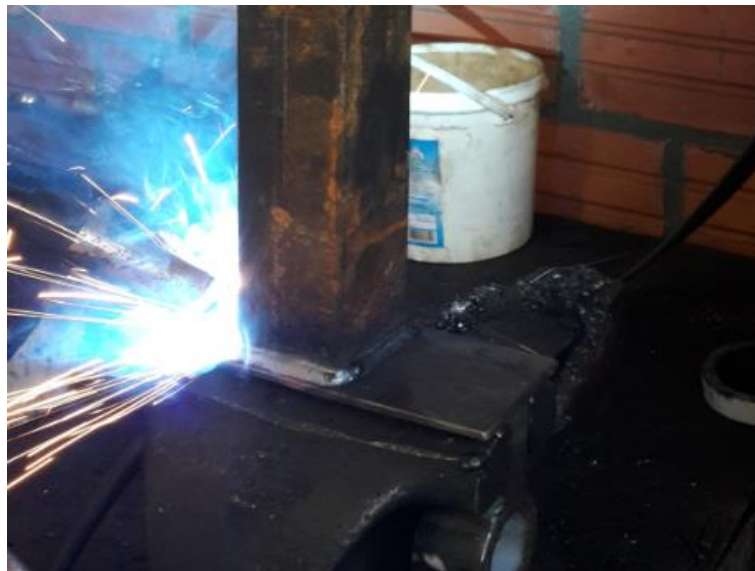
Soldagem do tubo quadrado a peça giratória.
